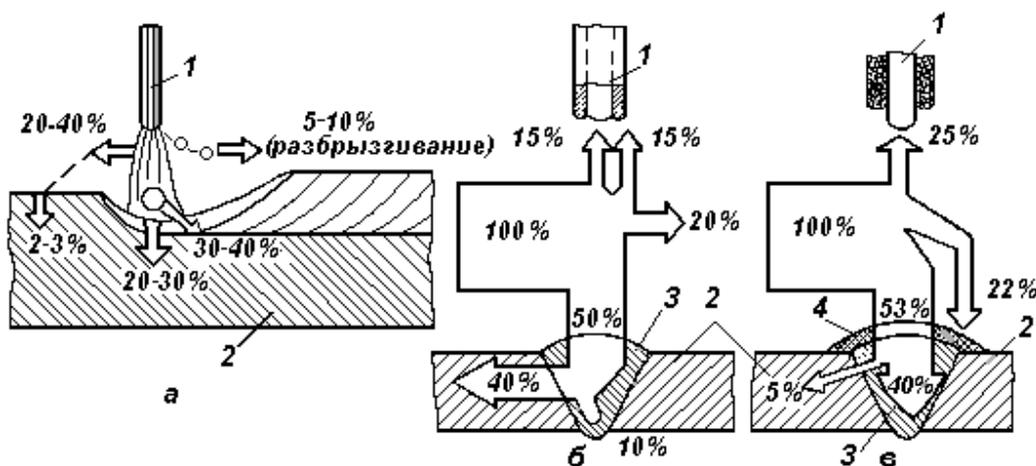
Тепловой баланс сварочной дуги
